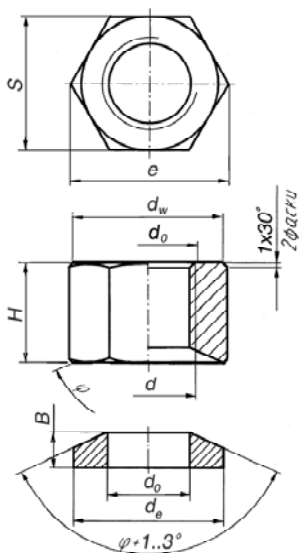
Гайка різьбового з'єднання з рівномірним розподіленням навантаження між витками - тип 1
